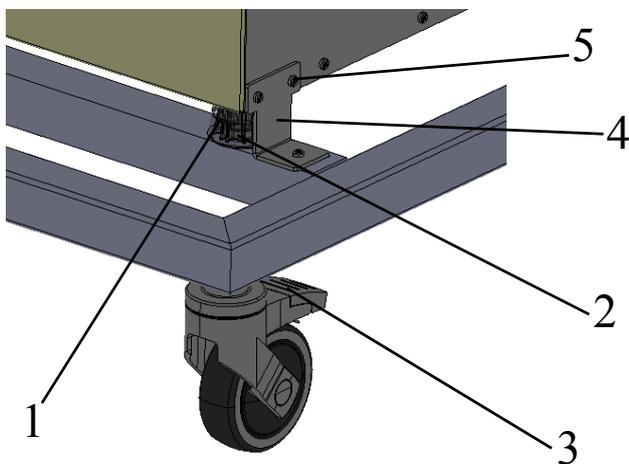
Armazón de apoyo con ruedas y sin pies de apoyo (versión i160 LK)
